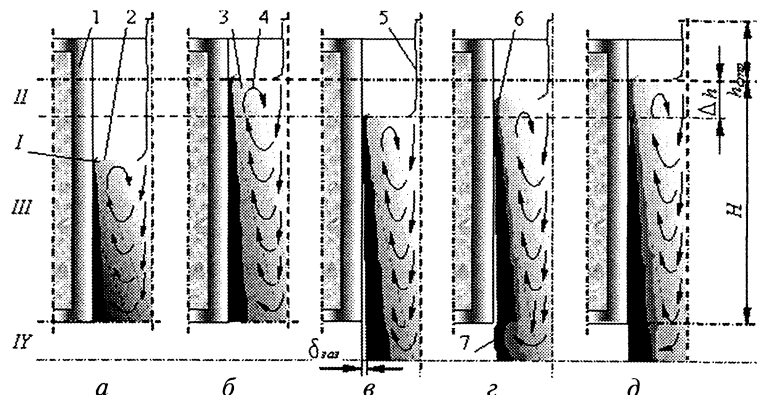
Механизм формирования начальной корки отливки: 1 — кристаллизатор; 2 — начальная корка; 3 — расплав; 4 — термоконвективные потоки; 5 — струя $h_{стр}$; 6 — вновь образующаяся корка; 7 — оплавление корки
